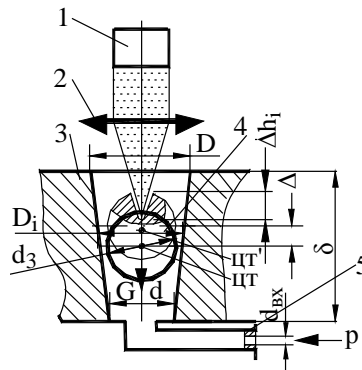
Схема обработки глубоких отверстий в заготовке простой формы (шар, цилиндр, диск). (1 – лазер; 2 – линза; 3 – стол; 4 – заготовка (шар); 5 – входная диафрагма).
